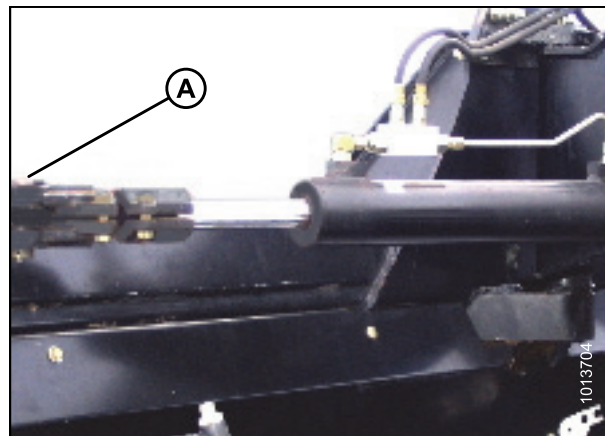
Прикрепленный шток цилиндра механизма управления
